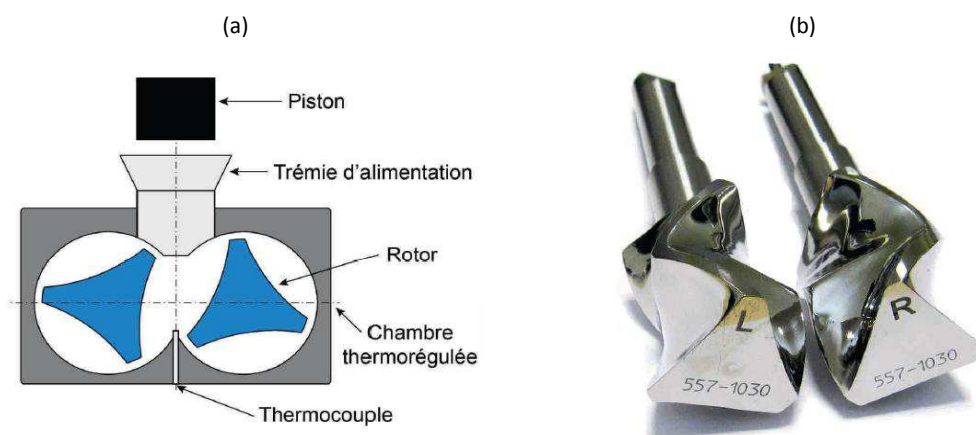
8. Schéma de la chambre du mélangeur interne (a) et photo des rotors roller (b)
